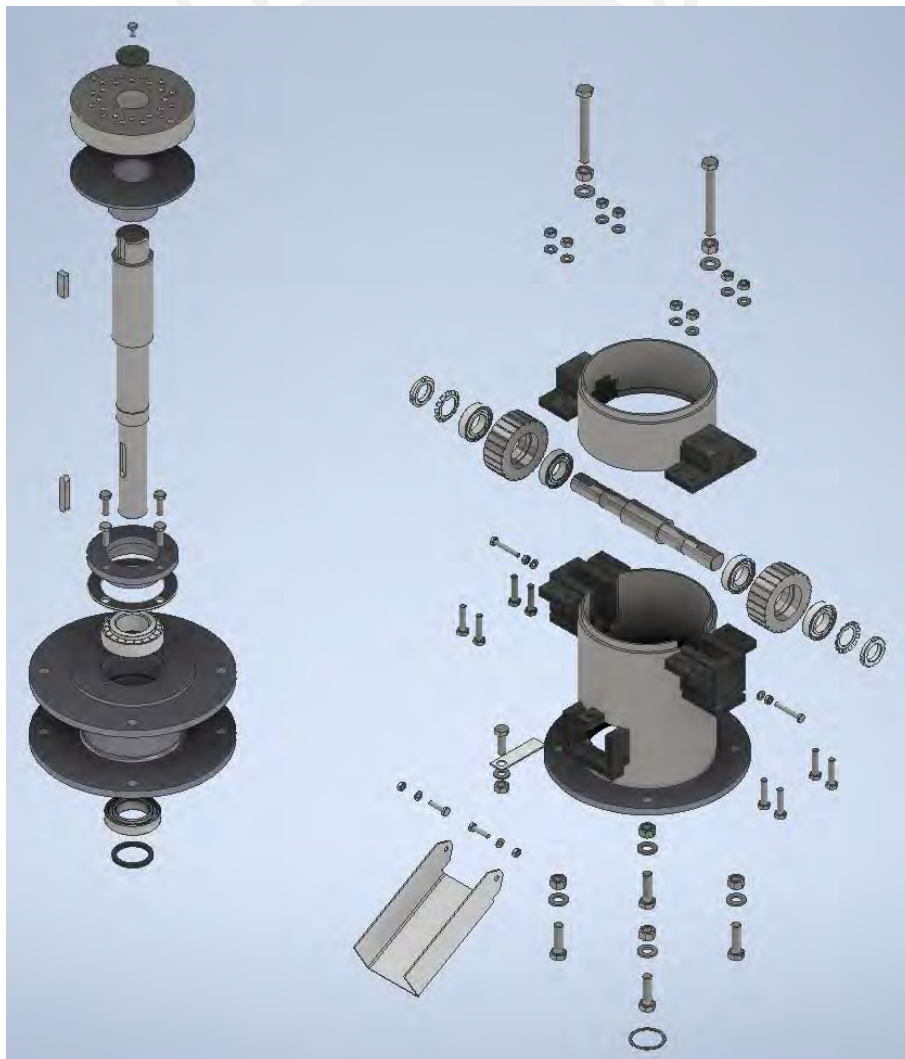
Vista explosionada del sistema de Extrusión en 3D.
